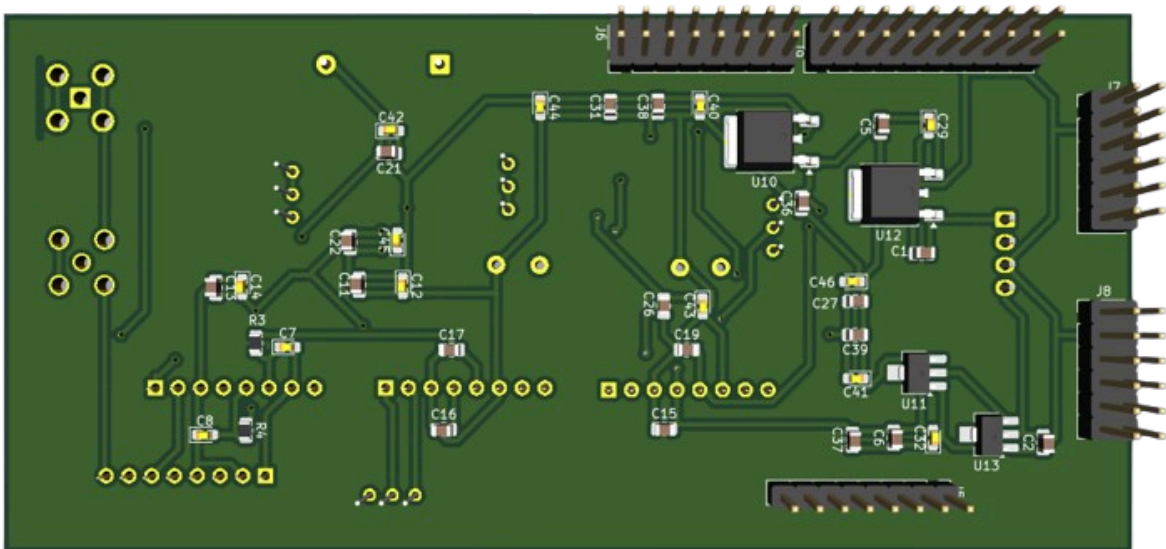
Capa inferior (Bottom Layer). Vista 3D del diseño de PCB de KiCad,
